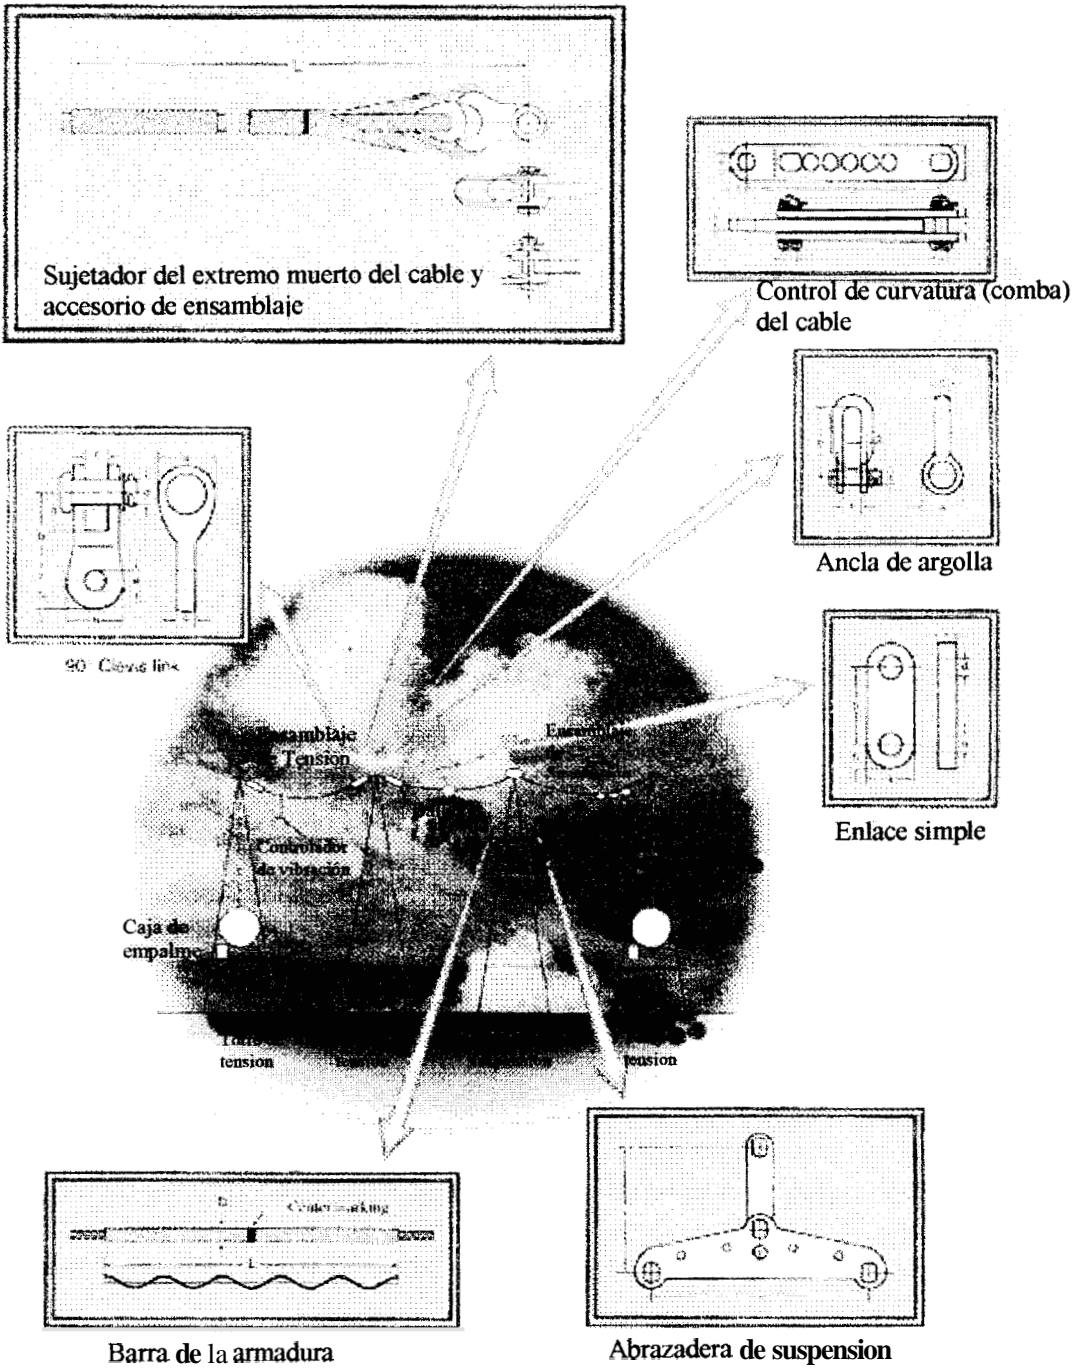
Accesorios para tendido de fibra opgw por tension o por suspension
